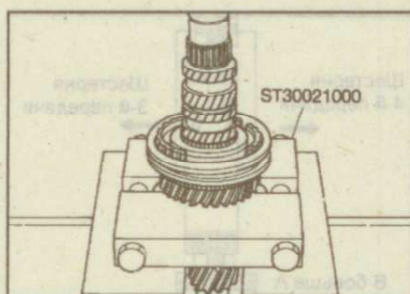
Снятие синхронизатора 3-й и 4-й передач и шестерни 3-й передачи с первичного вала
